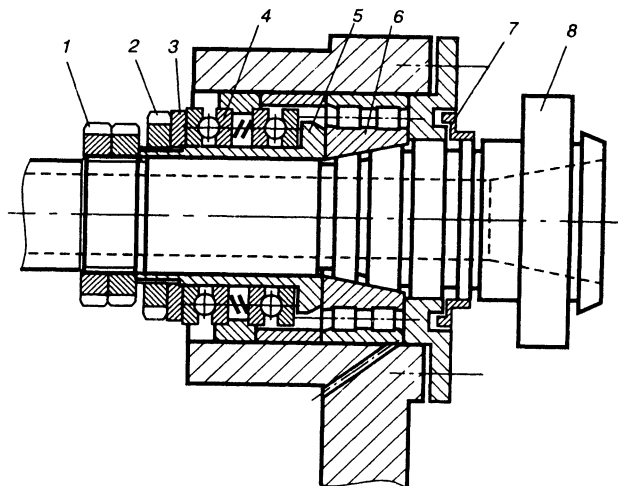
Устройство передней опоры шпинделя токарного станка:
